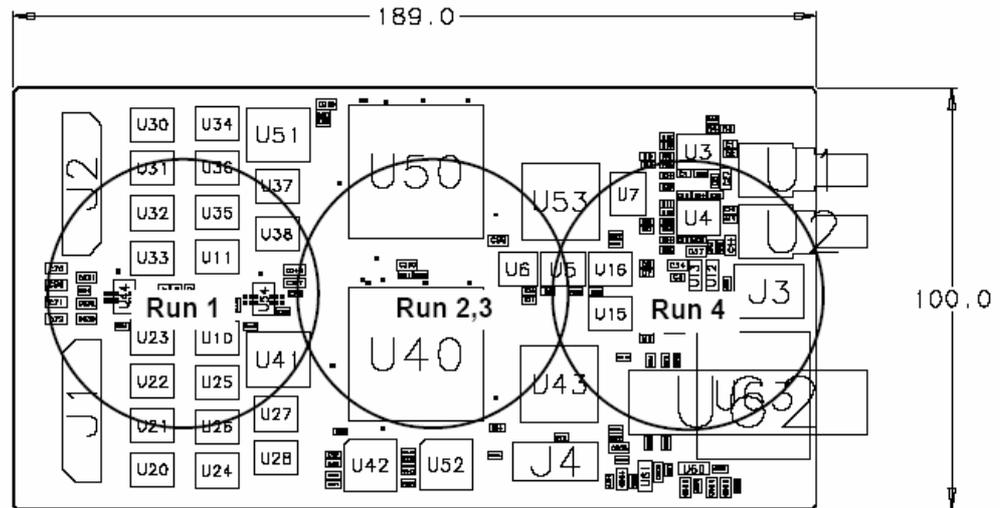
Posición del haz en la PCB de la Tarjeta.
